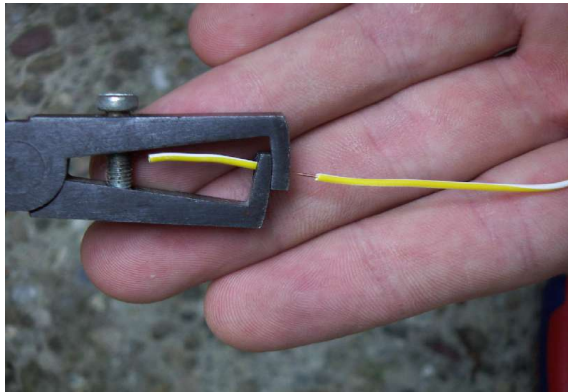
Abisolieren des Drahtes mit geeignetem Werkzeug
